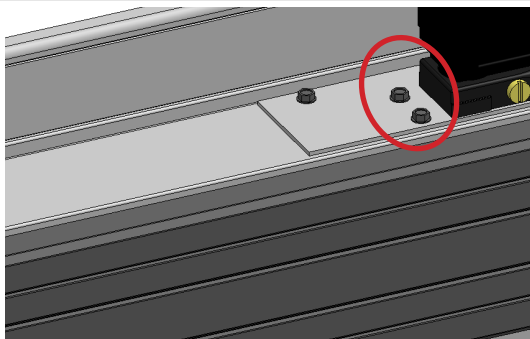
Vuelva a colocar los tornillos de la placa de transporte de la puerta.
